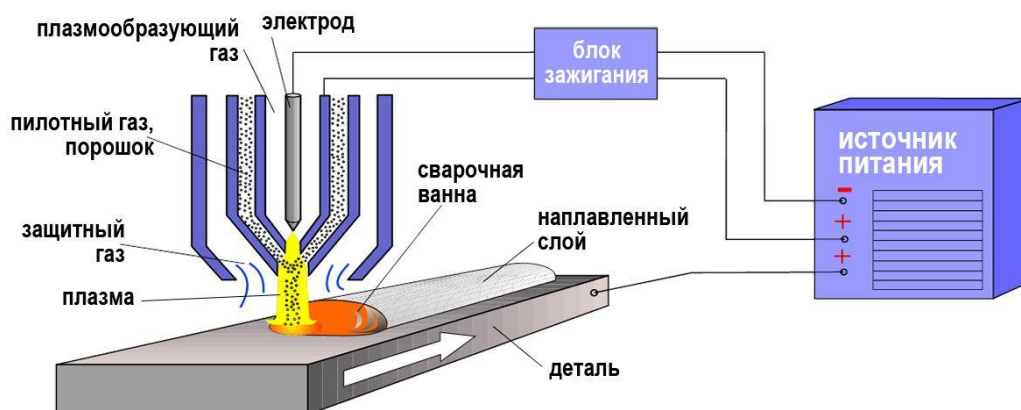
Принципиальная схема установки для электродуговой наплавки с газопорошковым армированием.
